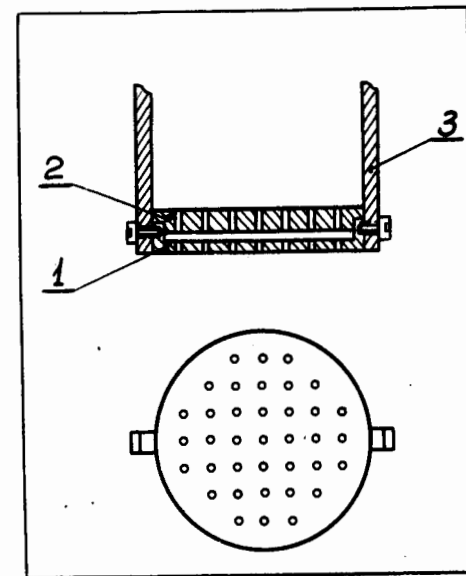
Фторопластовая кассета, 1,2 - крышки с отверстиями; 3 - держатель.
